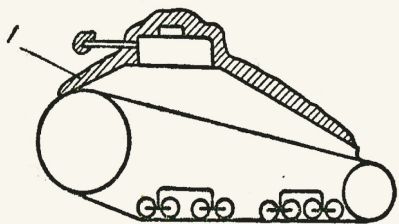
изображает различные типы противотанковых препятствий; фиг. 2 — танк, снабженный, согласно изобретению, рамой для осуществления прыжка через препятствие; фиг. 3 — схему движения такого танка во время прыжка; фиг. 4 — раму с пружинным упором для удлинения траектории прыжка; фиг. 5 — схему движения для случая танка, снабженного такой рамой; фиг. 6 — траекторию прыжка такого танка; фиг. 7 — различные типы препятствий с искусственным упором перед ними.
